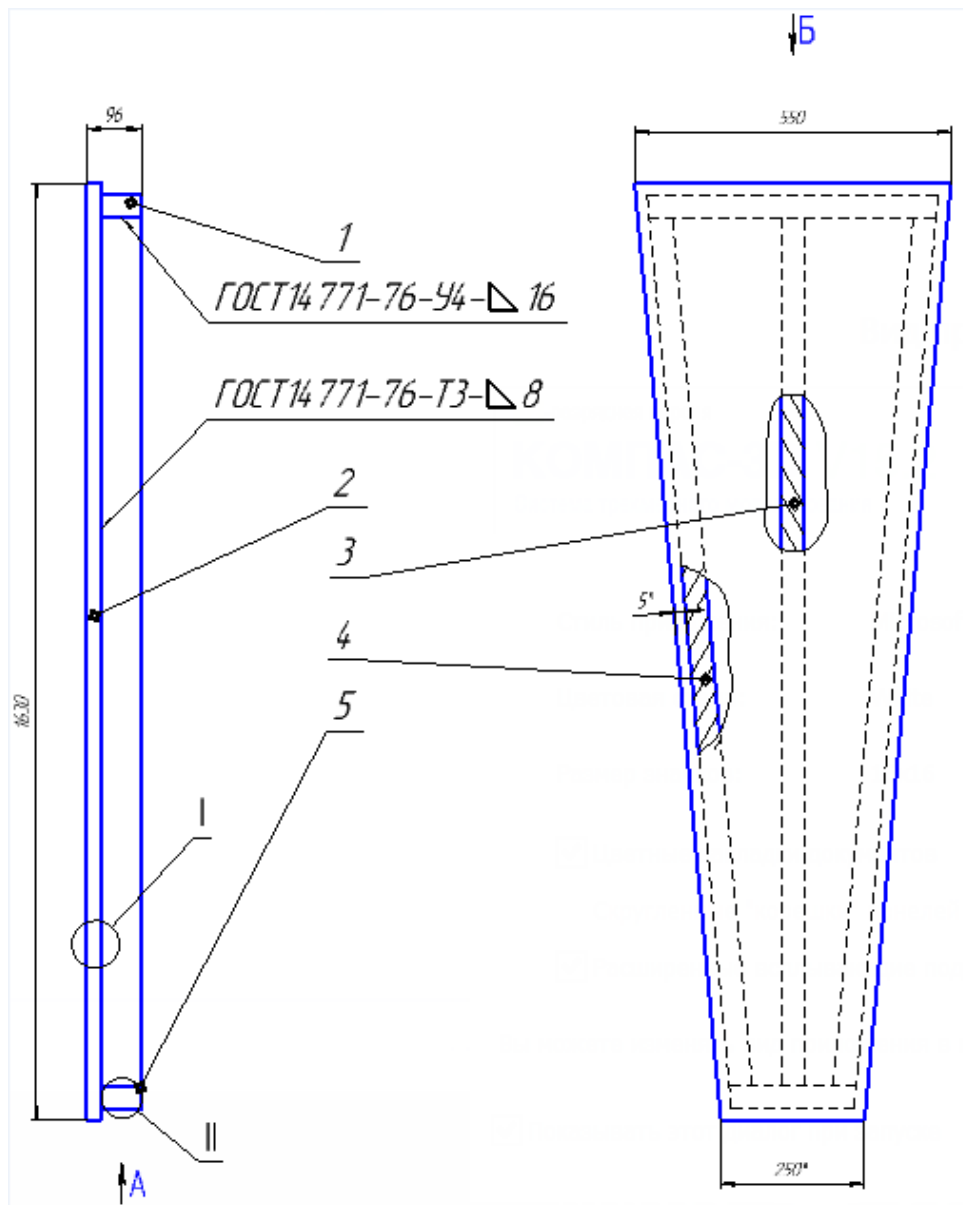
Эскиз сварного узла стенка
